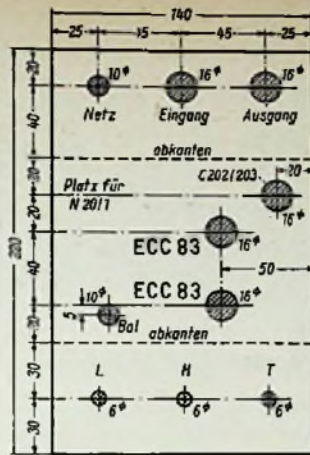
Chassis-Maße und Bohrplan für das SSTG 1
